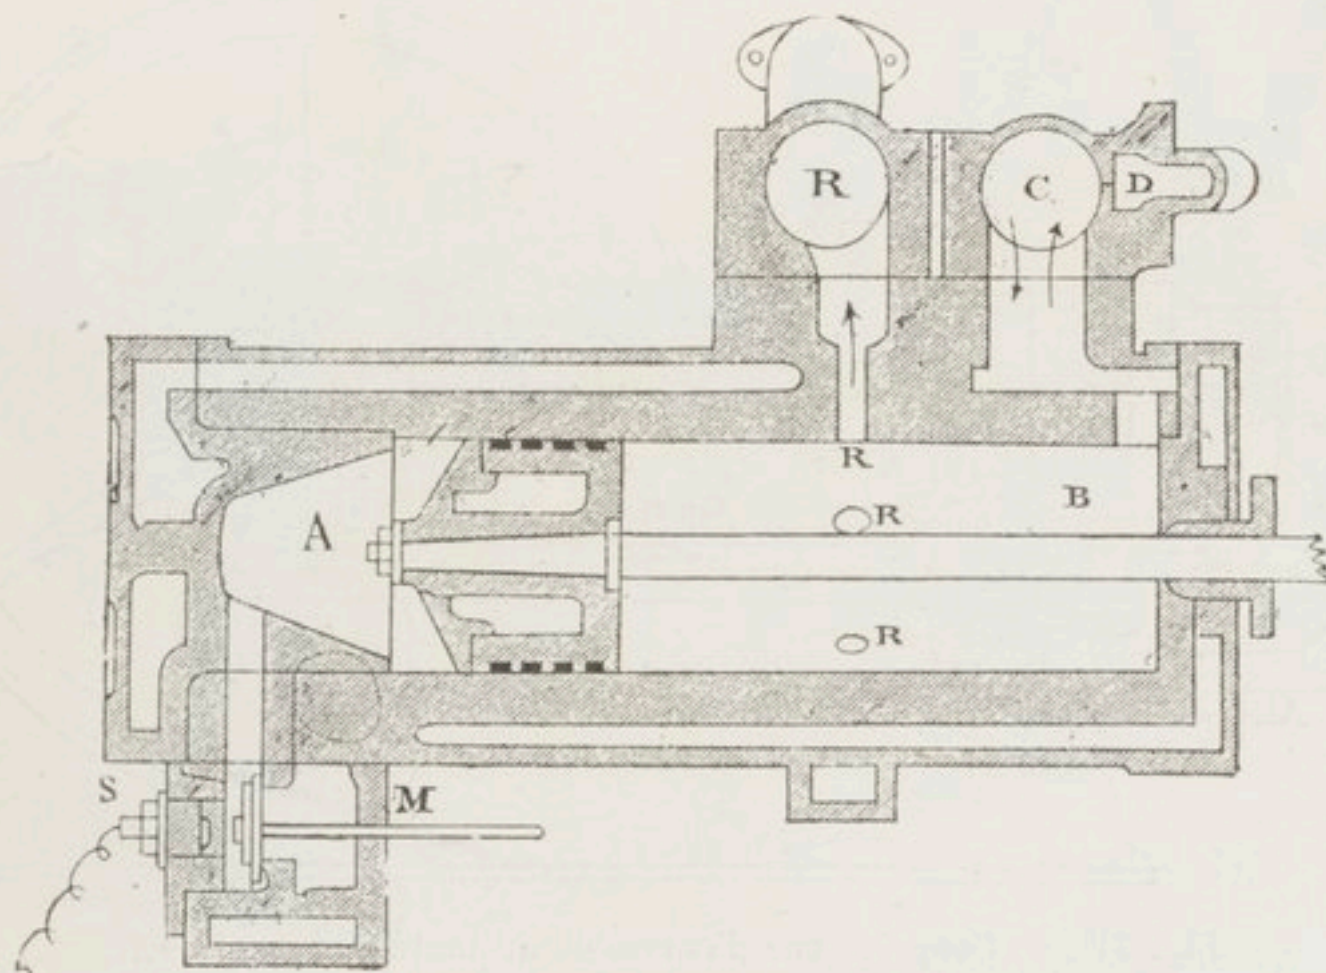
Coupe par l'axe du cylindre du moteur à gaz Ravel.
